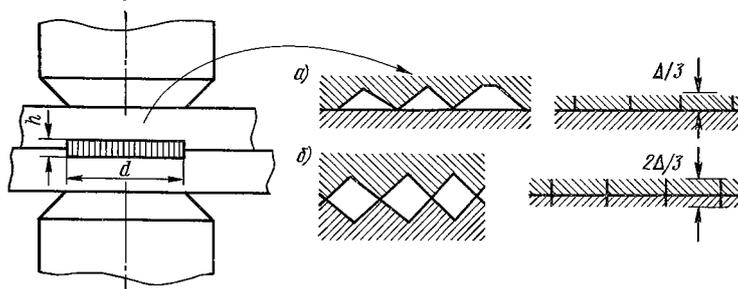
Схема деформации пирамид шероховатости при точечной сварке и формирование из них расплавленного диска высотой  $h = (1/3 + 2/3) \Delta$
